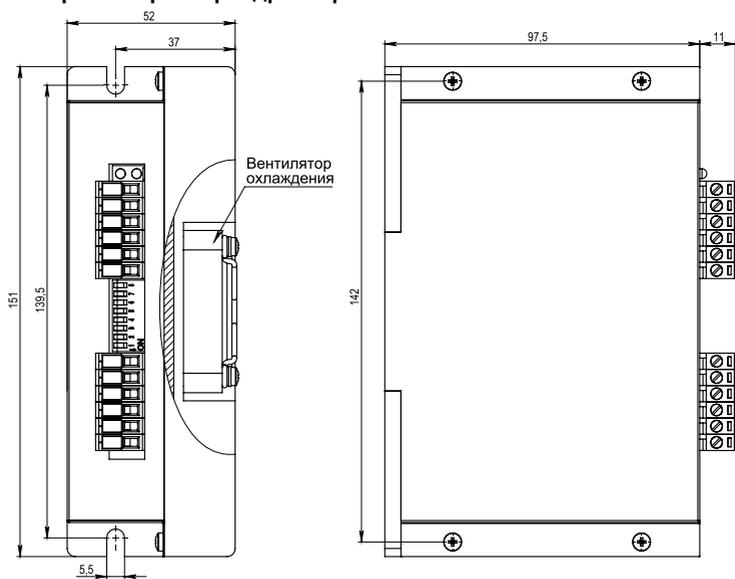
габаритные размеры драйверов SMD-20.34.60
